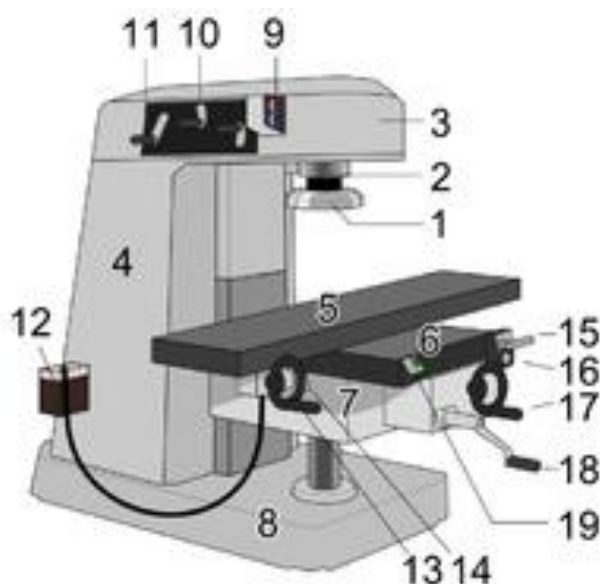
Вертикально-фрезерный станок (1 — фреза, 2 — шпиндель, 3 — хобот, 4 — станина, 5 — стол, 6 — салазки, 7 — консоль, 8 — фундаментная плита)
